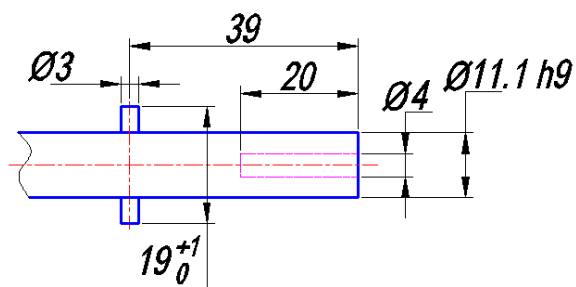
Присоединительные размеры контактного разъёма А33
